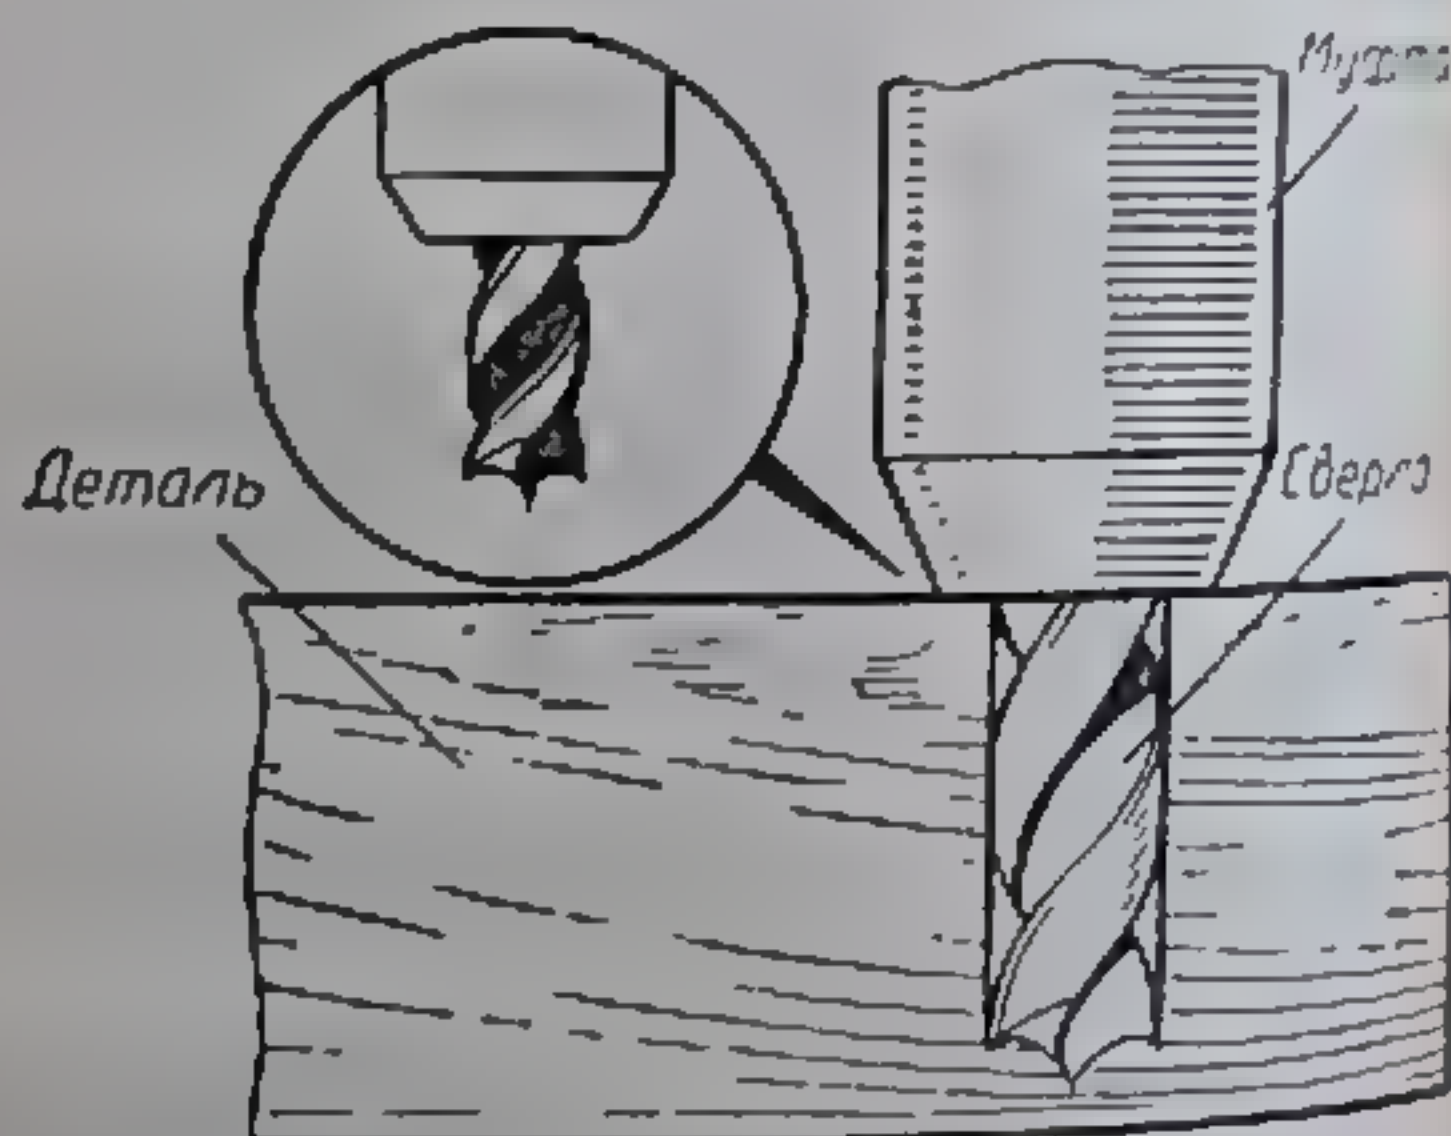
Муфта на сверло для контроля глубины отверстия.
